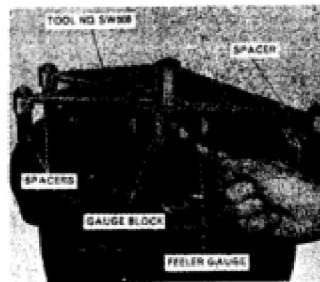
Controle as behuizing, eindaandrijving en remassemblage voor juiste differentiële drager lagershim dikte. Raadpleeg tekst.
